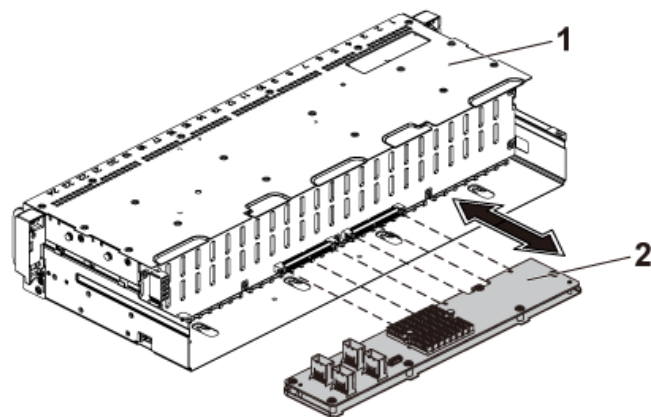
Retrait et installation de l'ensemble carte d'extenseur de disque dur de 2,5 pouces du bâti de disque dur
